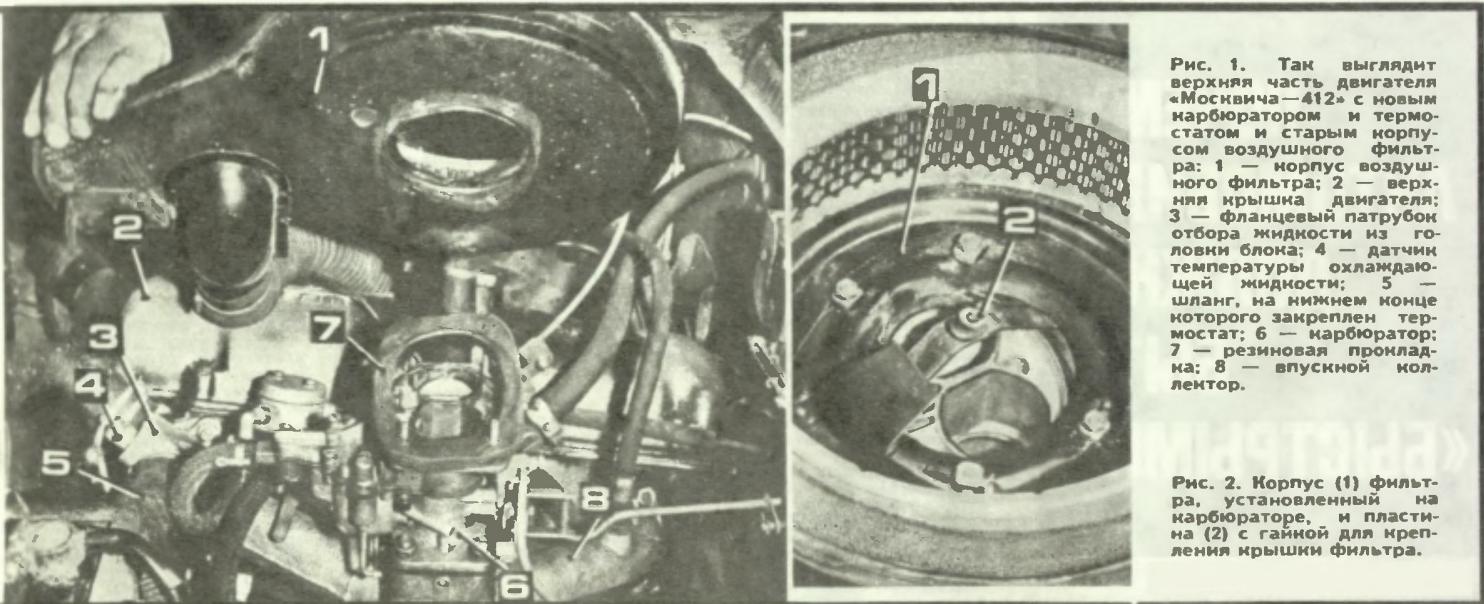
Так выглядит верхняя часть двигателя «Москвича-412» с новым карбюратором и термостатом и старым корпусом воздушного фильтра: 1 — корпус воздушного фильтра; 2 — верхняя крышка двигателя; 3 — фланцевый патрубок отбора жидкости из головки блока; 4 — датчик температуры охлаждающей жидкости; 5 — шланг, на нижнем конце которого закреплен термостат; 6 — карбюратор; 7 — резиновая прокладка; 8 — впускной коллектор.
